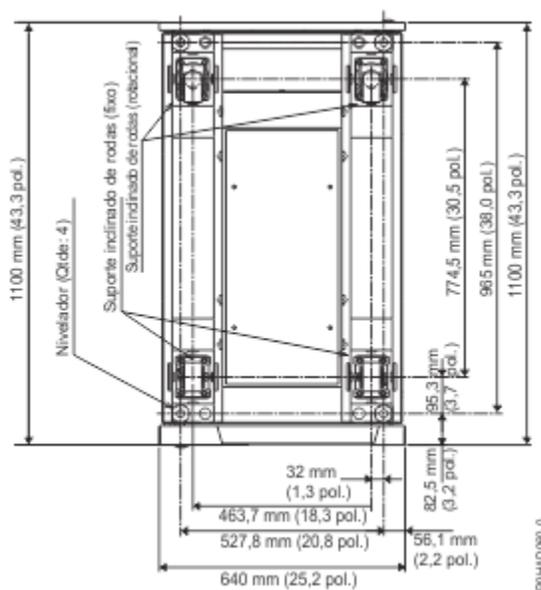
Locais do suporte inclinado de rodas e do nivelador
